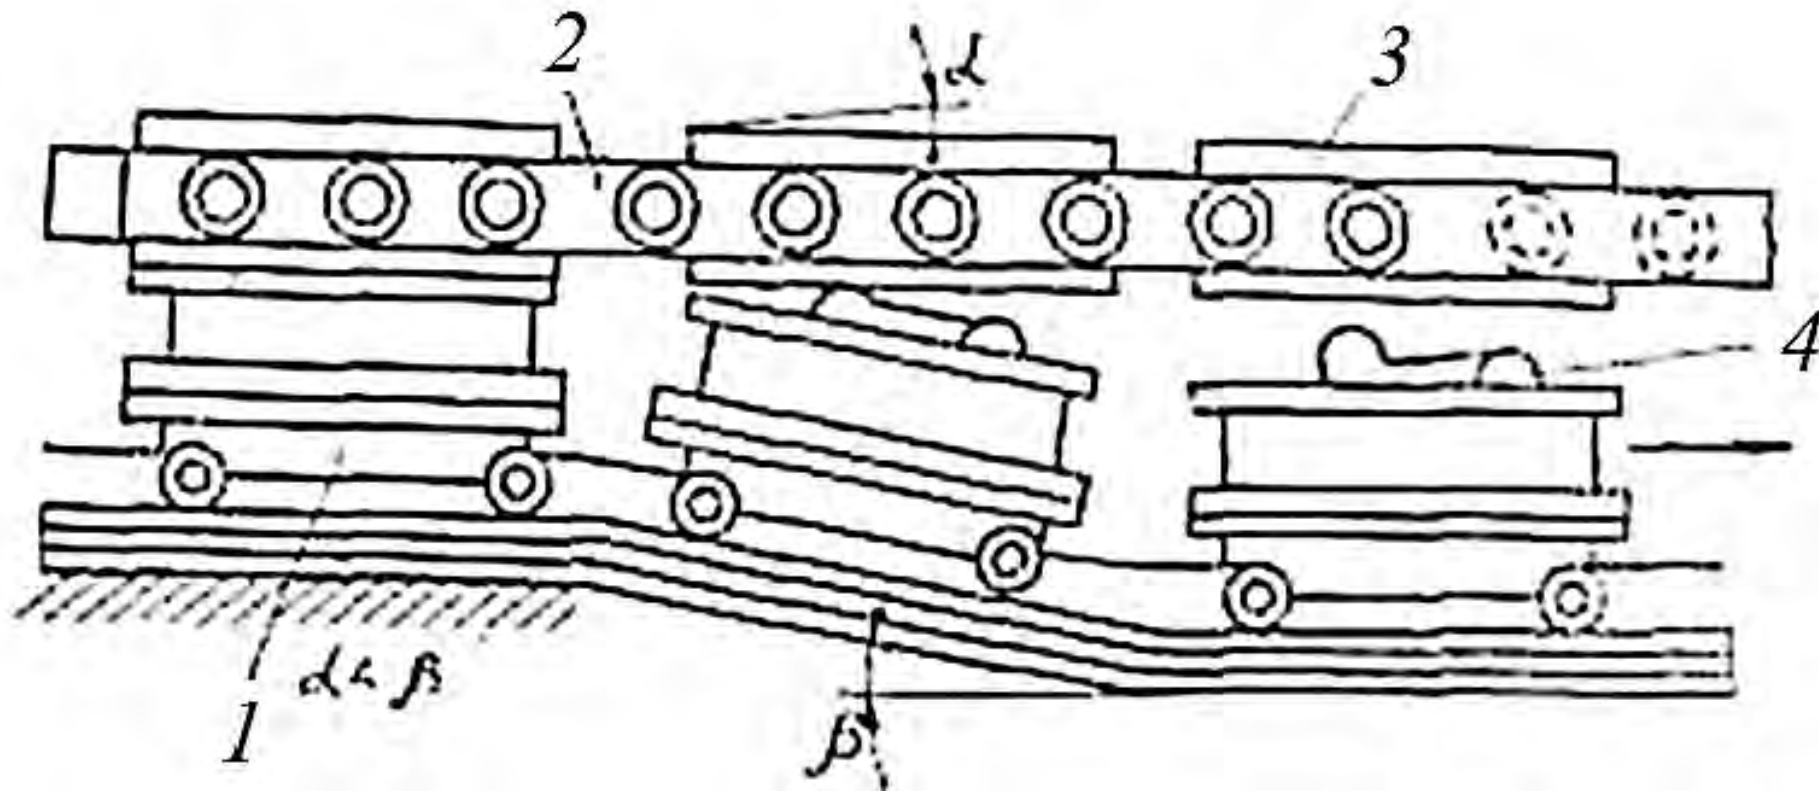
Схема распаровщика непрерывного действия с кромочным рольгангом: 1 – тележка конвейера; 2 – кромочный рольганг; 3 – опорные выступы верхней опоки; 4 – отливка
